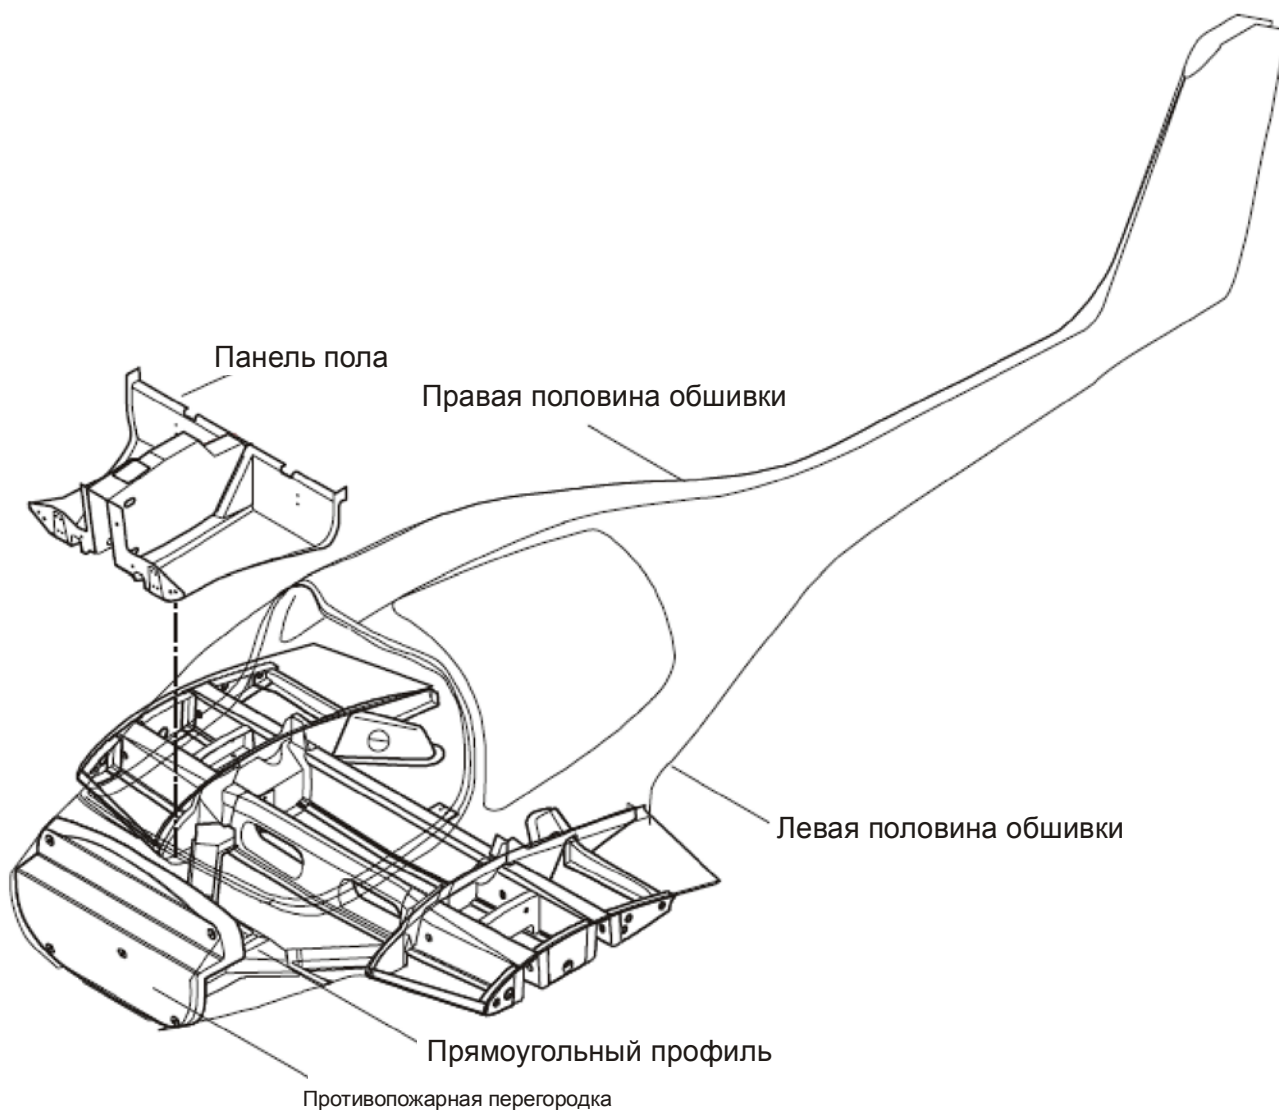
Половины обшивки фюзеляжа и конструкция носовой части фюзеляжа
